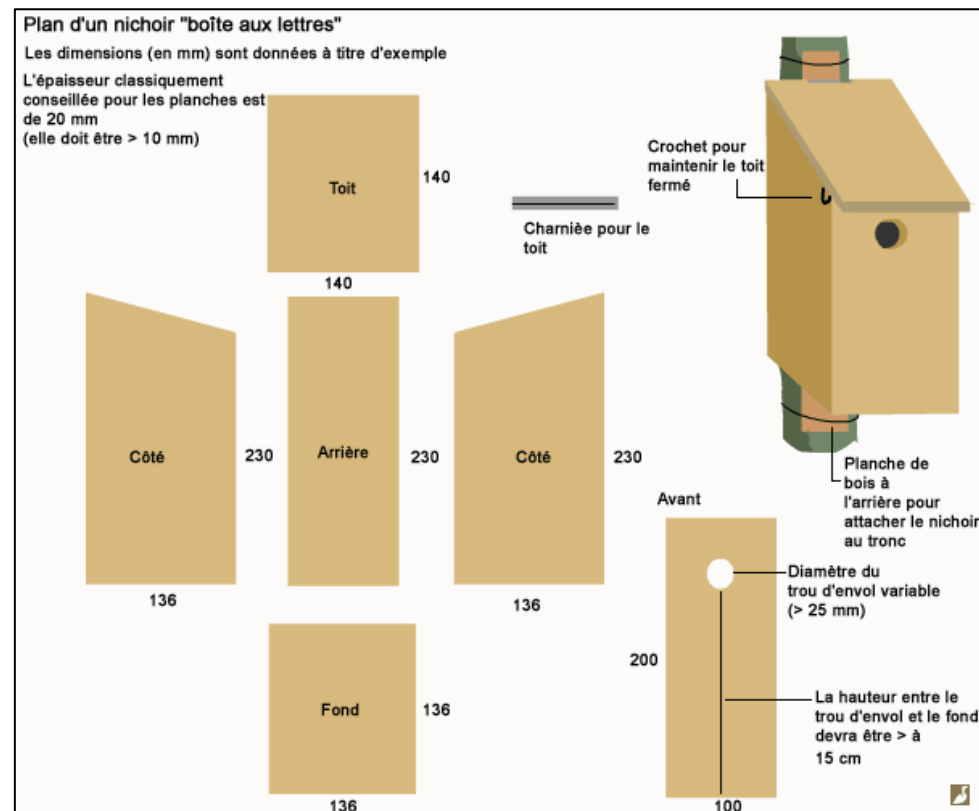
Plan de fabrication d'un nichoir type « boîte aux lettres » permettant d'accueillir des petits passereaux (source : jardiner-autrement.fr).
